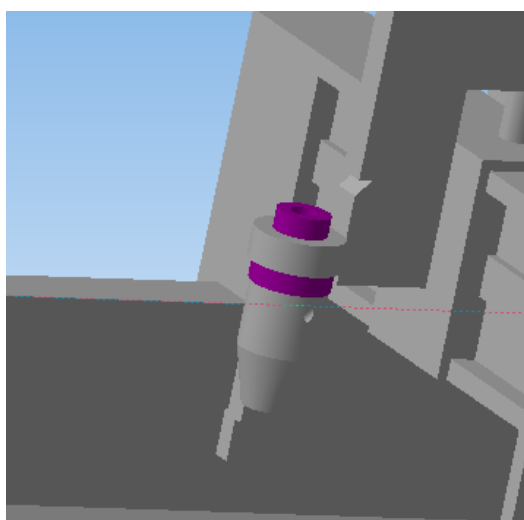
3D-модель инструмента для гидроабразивной резки
